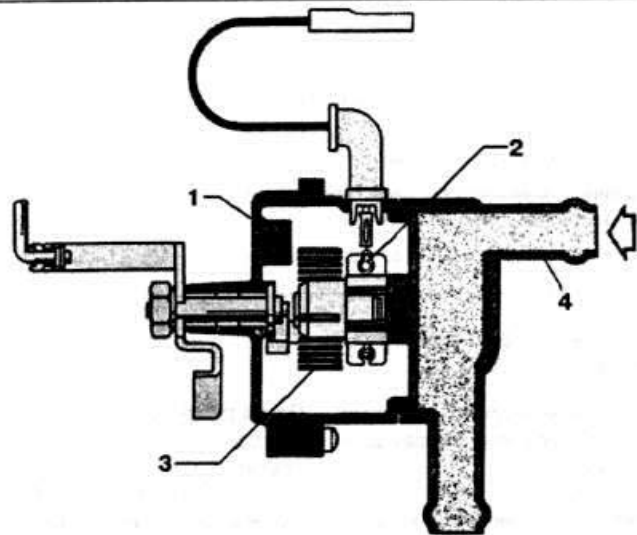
Разрез корпуса автоматического пускового устройства:
